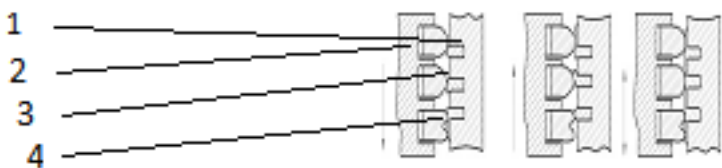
Схема образования плёнки на поверхности гильзы цилиндров: 1-поршень; 2-поршневое кольцо; 3-гильза цилиндров; 4-вставка
